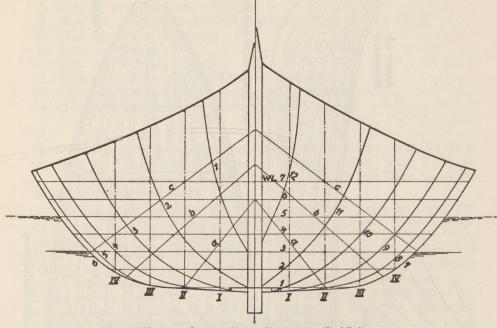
Spantenriß des Bootes von Mechlinfen.
